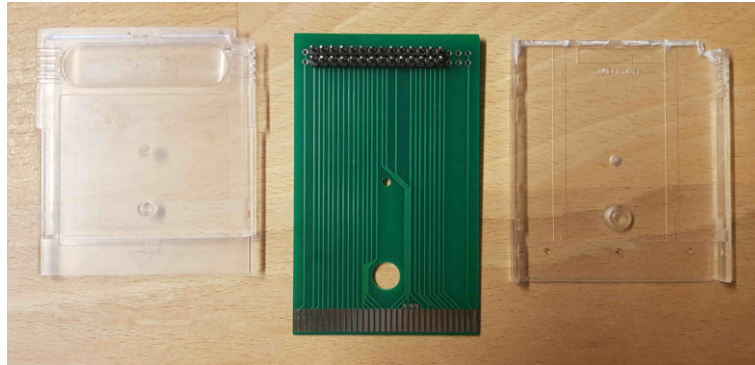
PCB zum Testen der Cartridge-PCB
